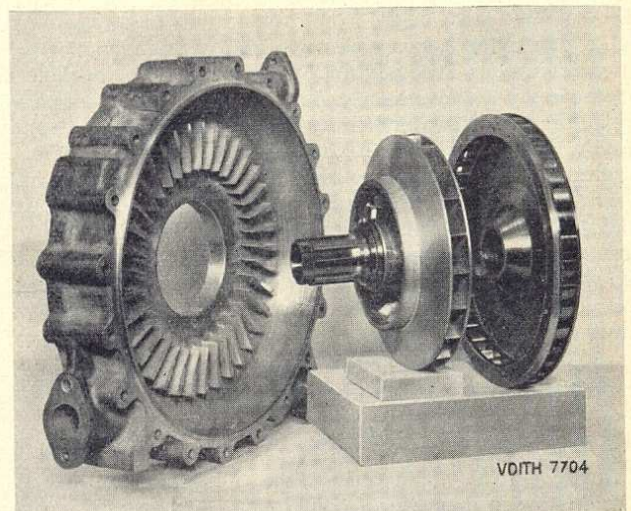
Die Schaufelräder des Föttinger-Wandlers. Leitschaufelkranz mit Gehäuse, Pumpen- und Turbinenlaufrad
